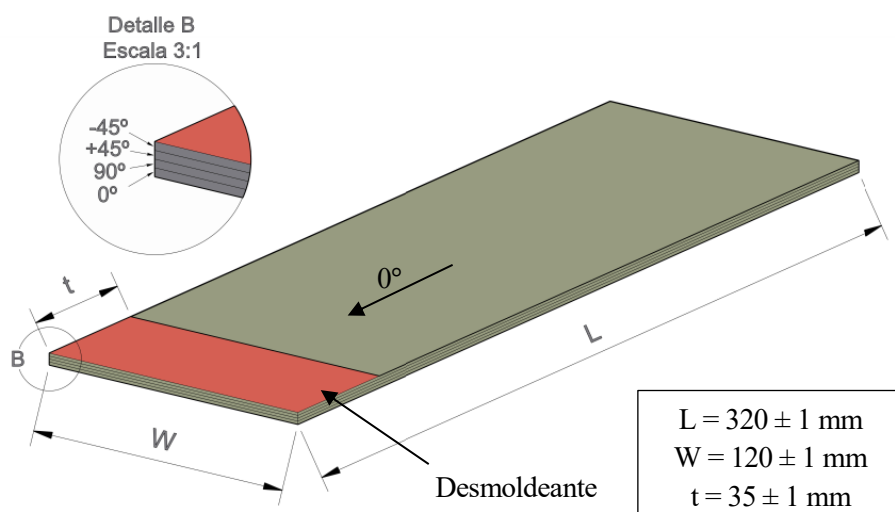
Apilado de la lámina desmoldeante del extremo del panel 1
